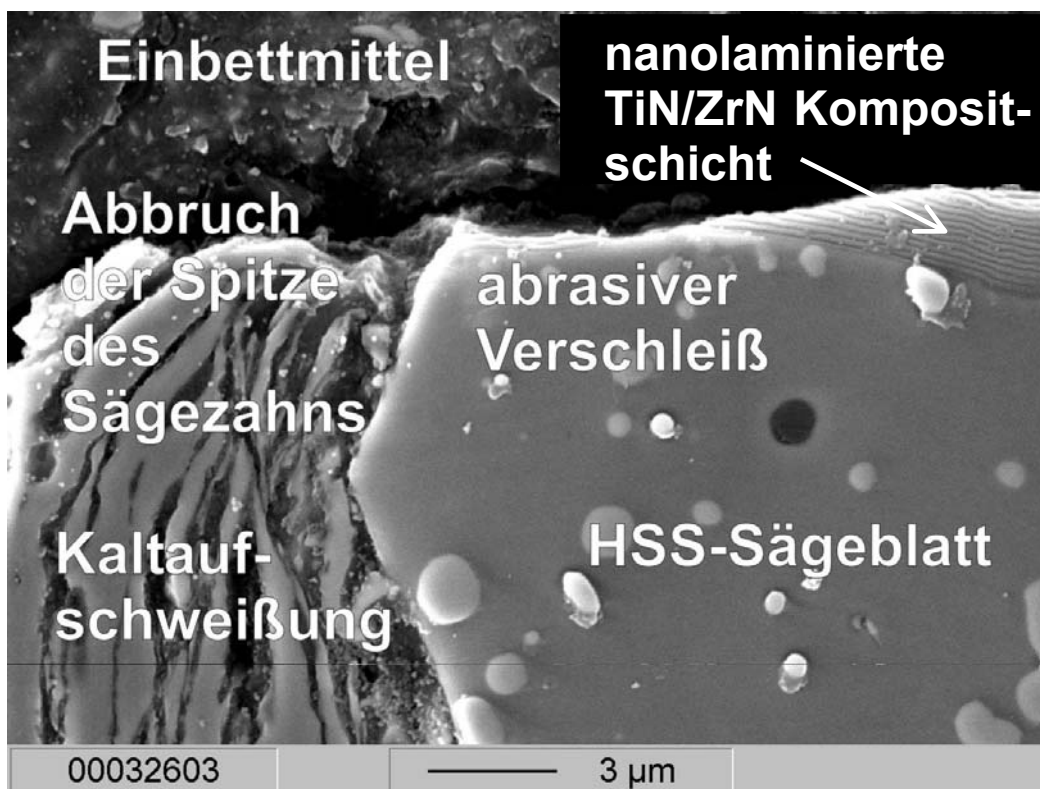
REM-Aufnahme der Bruchfläche der Spitze eines Sägeblatts mit Kaltaufschweißung.
